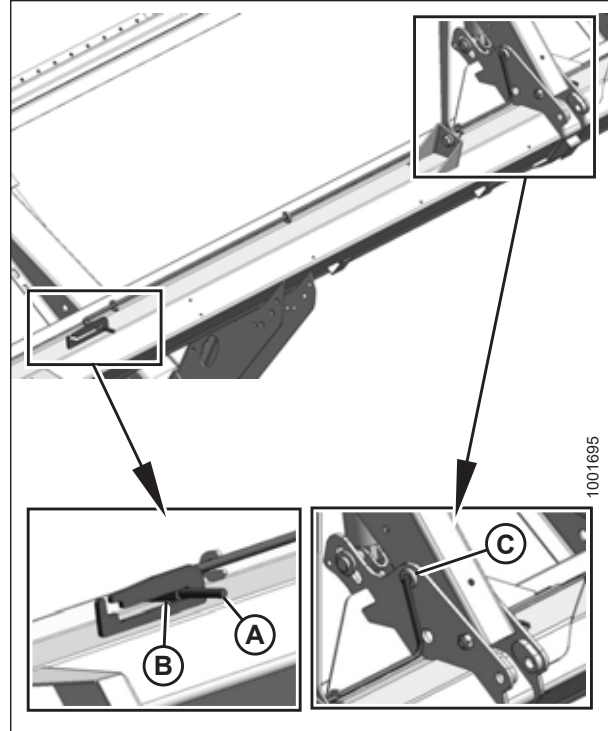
Запобіжний упор мотовила — центральний важіль
